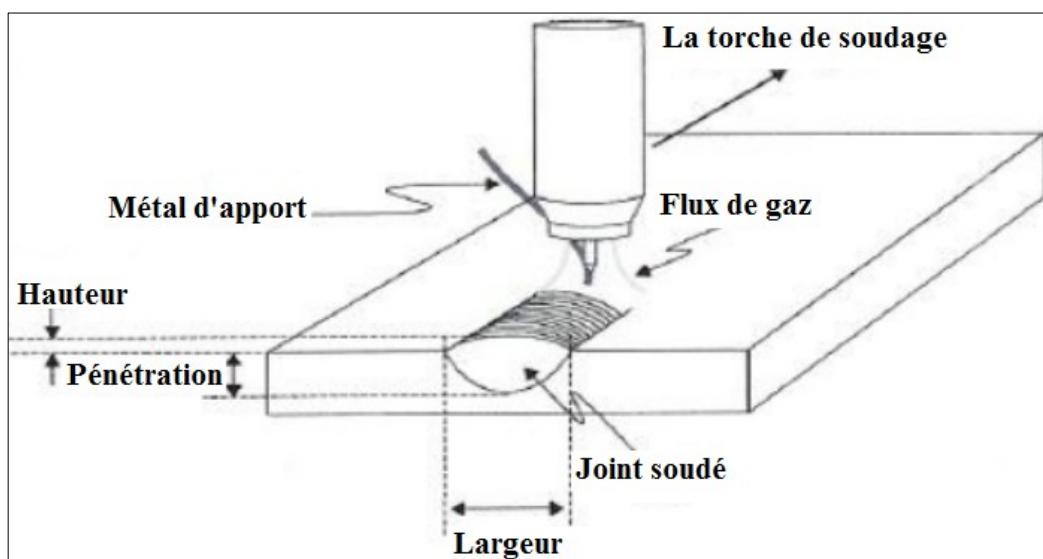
Procédure de soudage par TIG [82].
